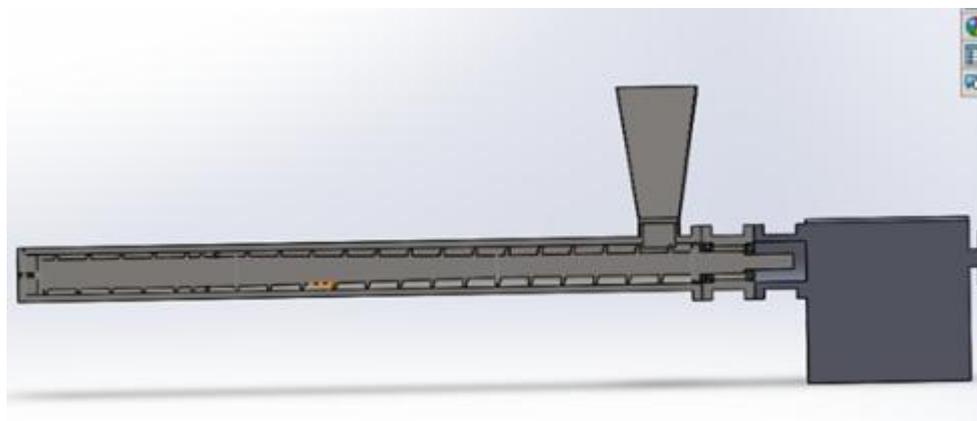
Image présenté par SolidWorks de la machine extrudeuse
